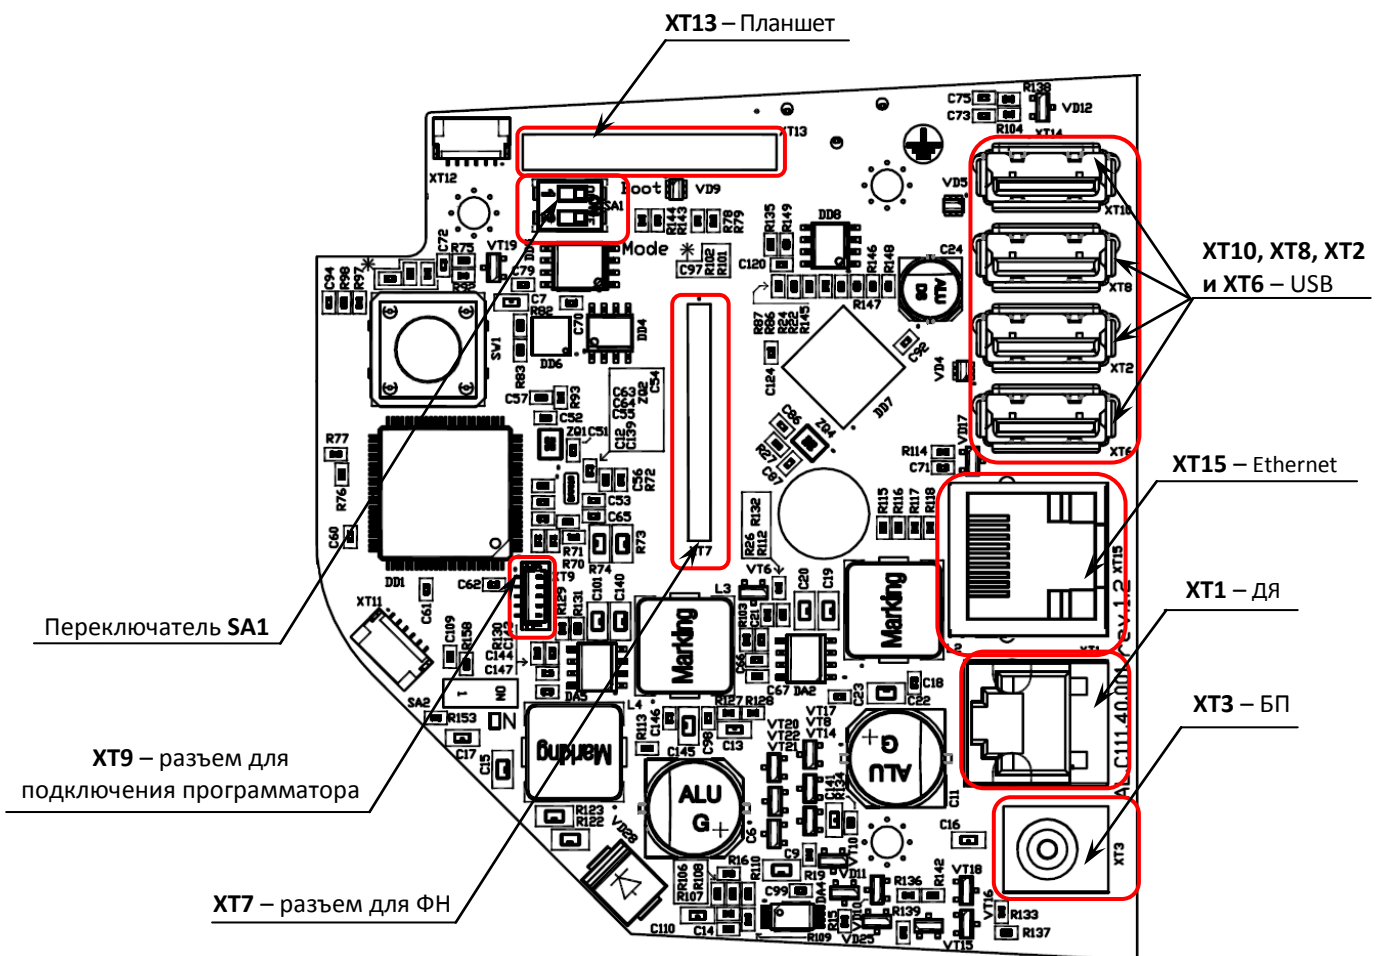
Расположение элементов блока управления AL.C111.40.000 (вид сверху)
